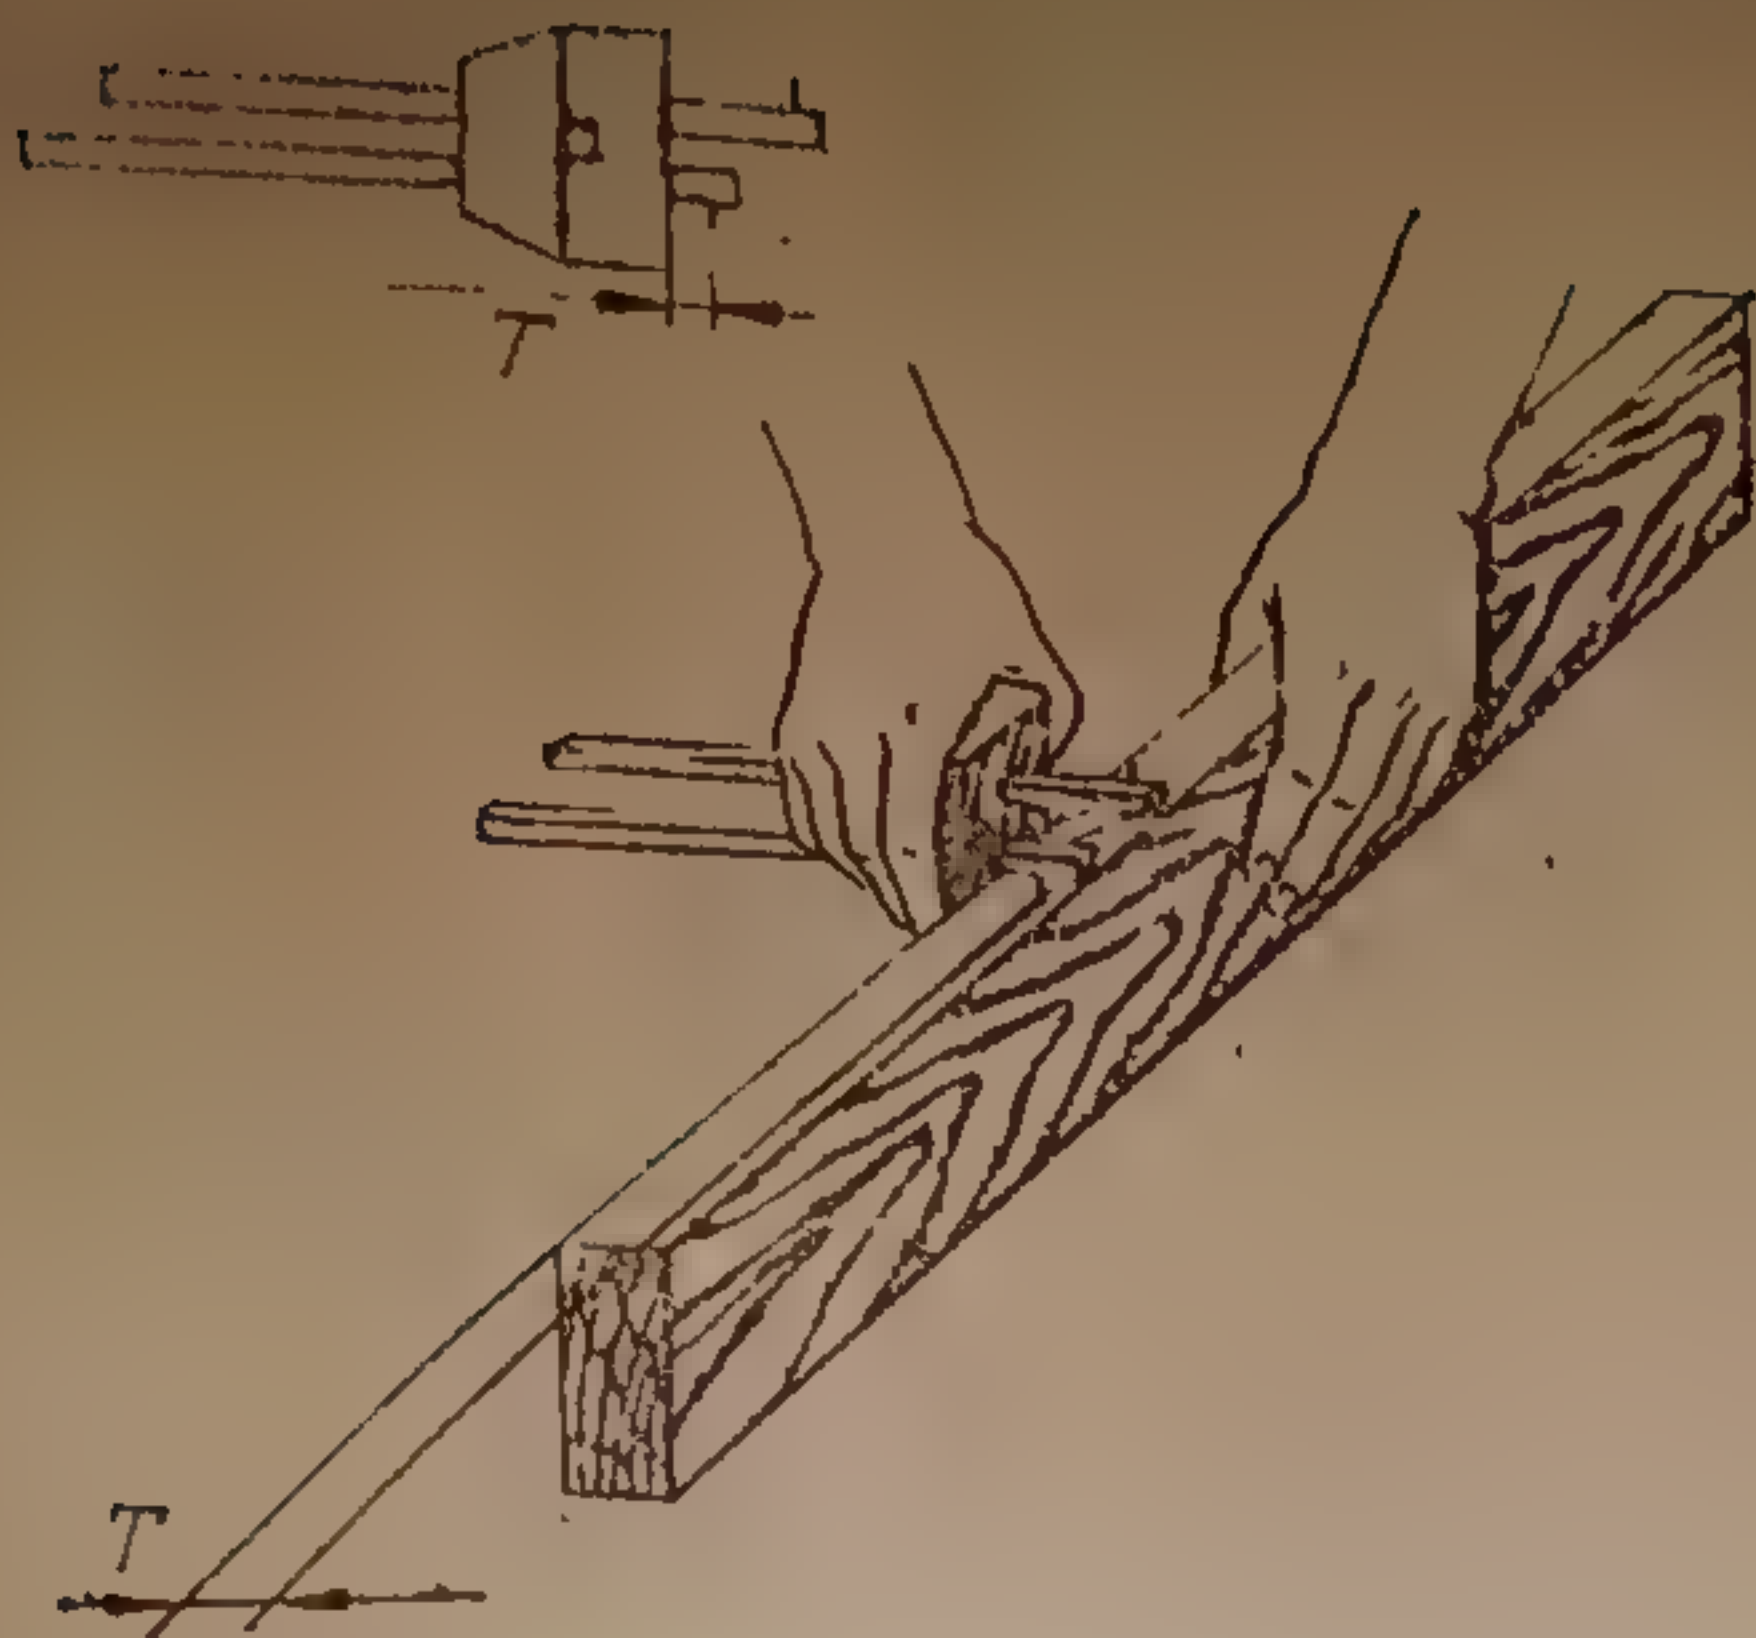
Разметка толщины заготовки с помощью рейсмуса
